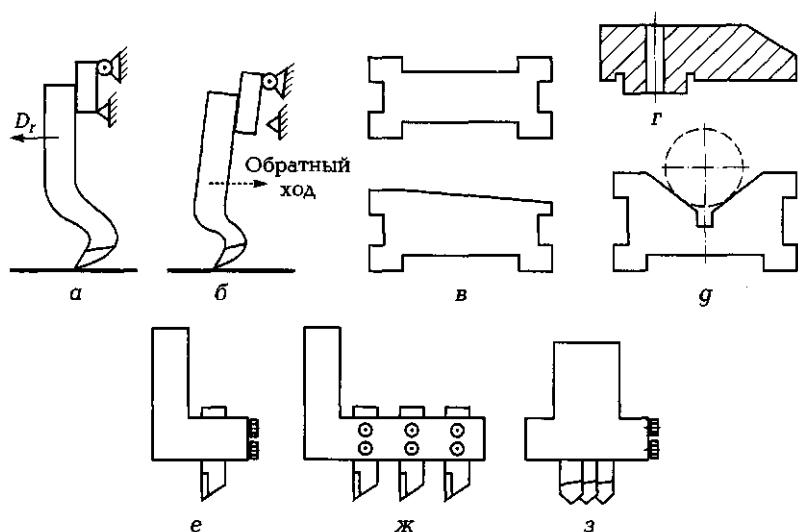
Рабочие приспособления для строгальных и долбежных станков:
